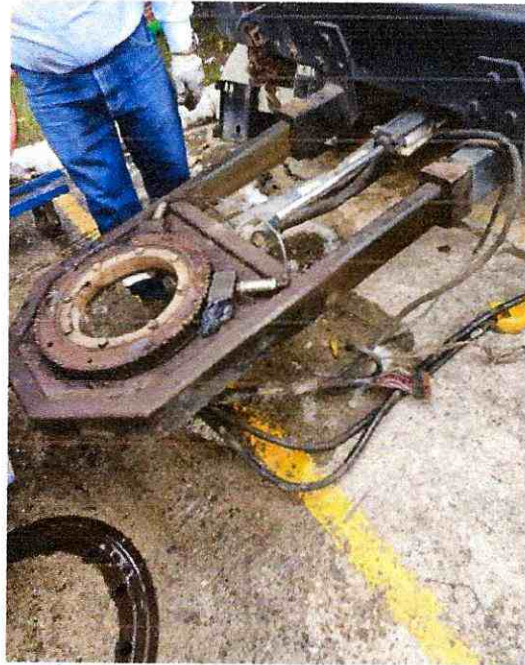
Desmonte carretel, revisión rodamientos lineal y rotativo
